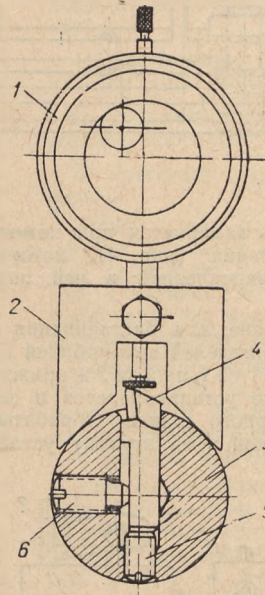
Приспособление для замера вылета резца: 1 — индикатор; 2 — призма; 3 — расточная скалка; 4 — резец; 5 — винт регулировочный; 6 — винт стопорный.
